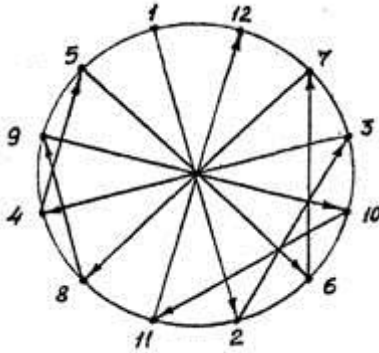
Схема затягування болтів фланцевого з'єднання
